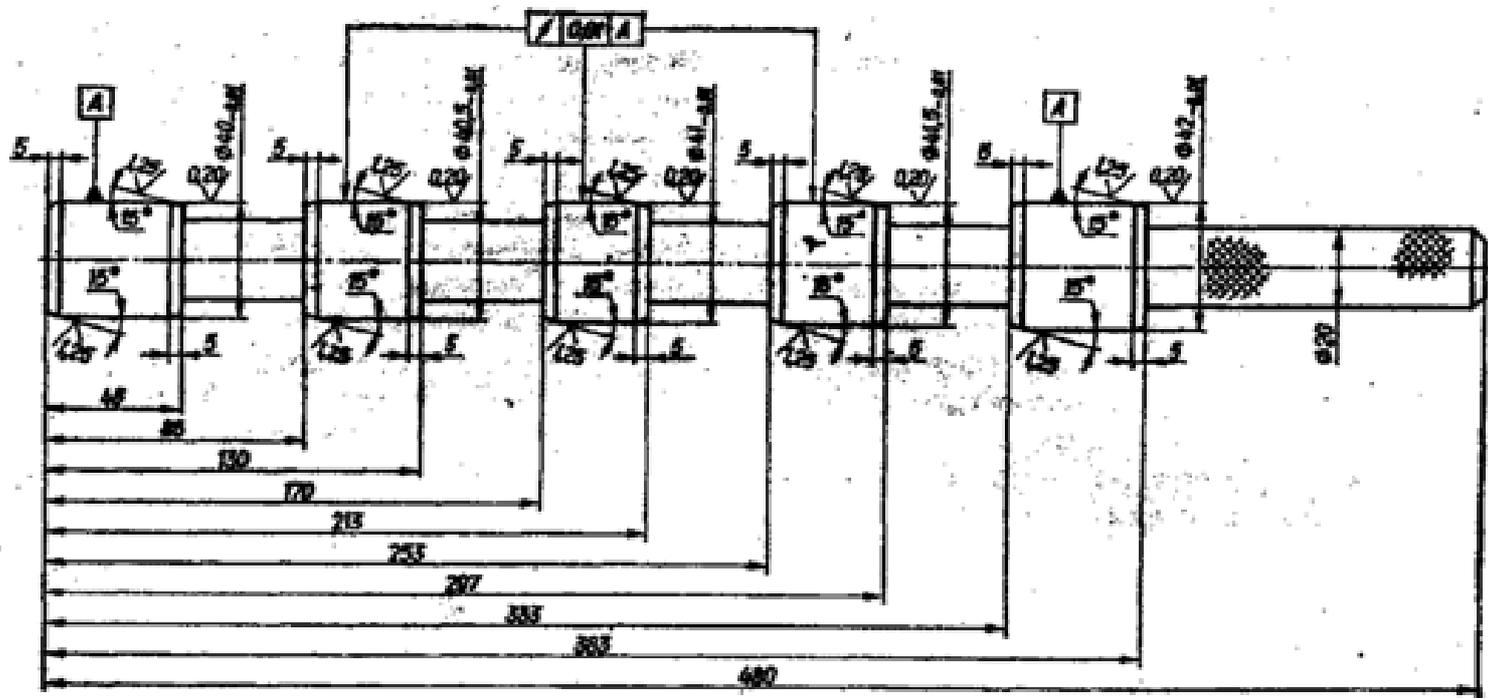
Оправка для проверки соосности подшипников распределительного вала
